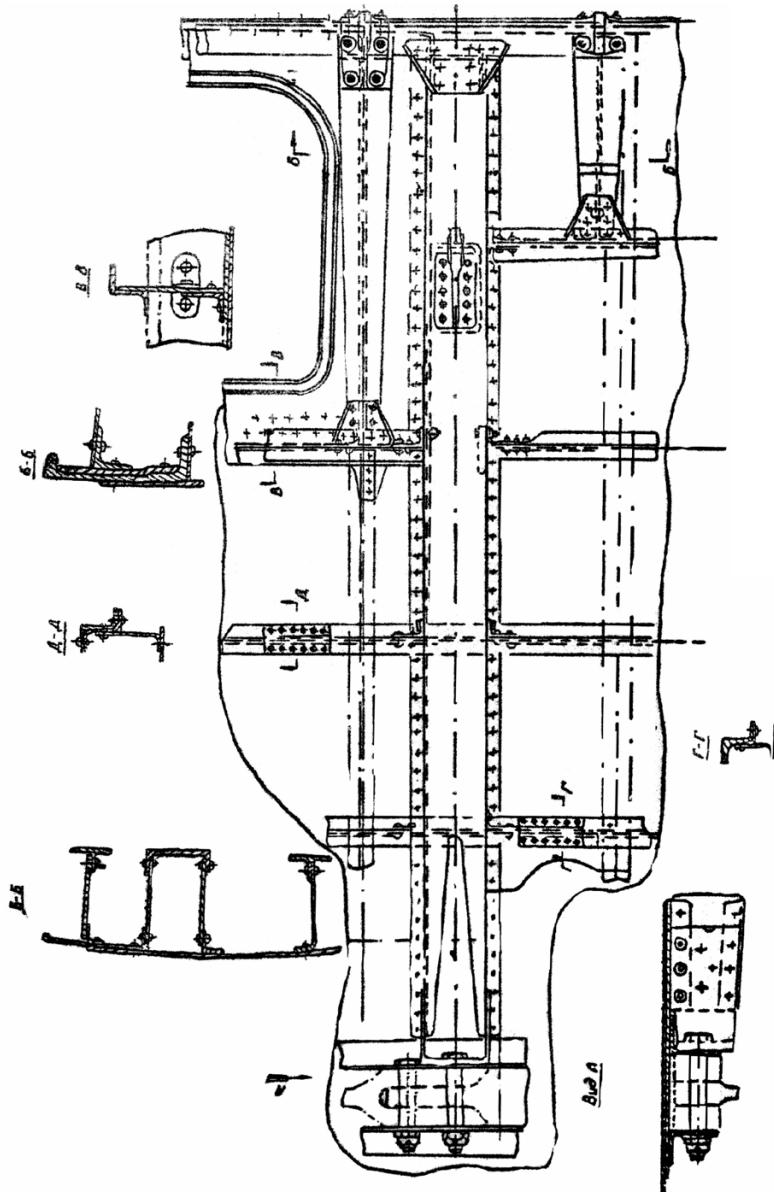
Стыковка балок крепления двигателя с каркасом фюзеляжа
